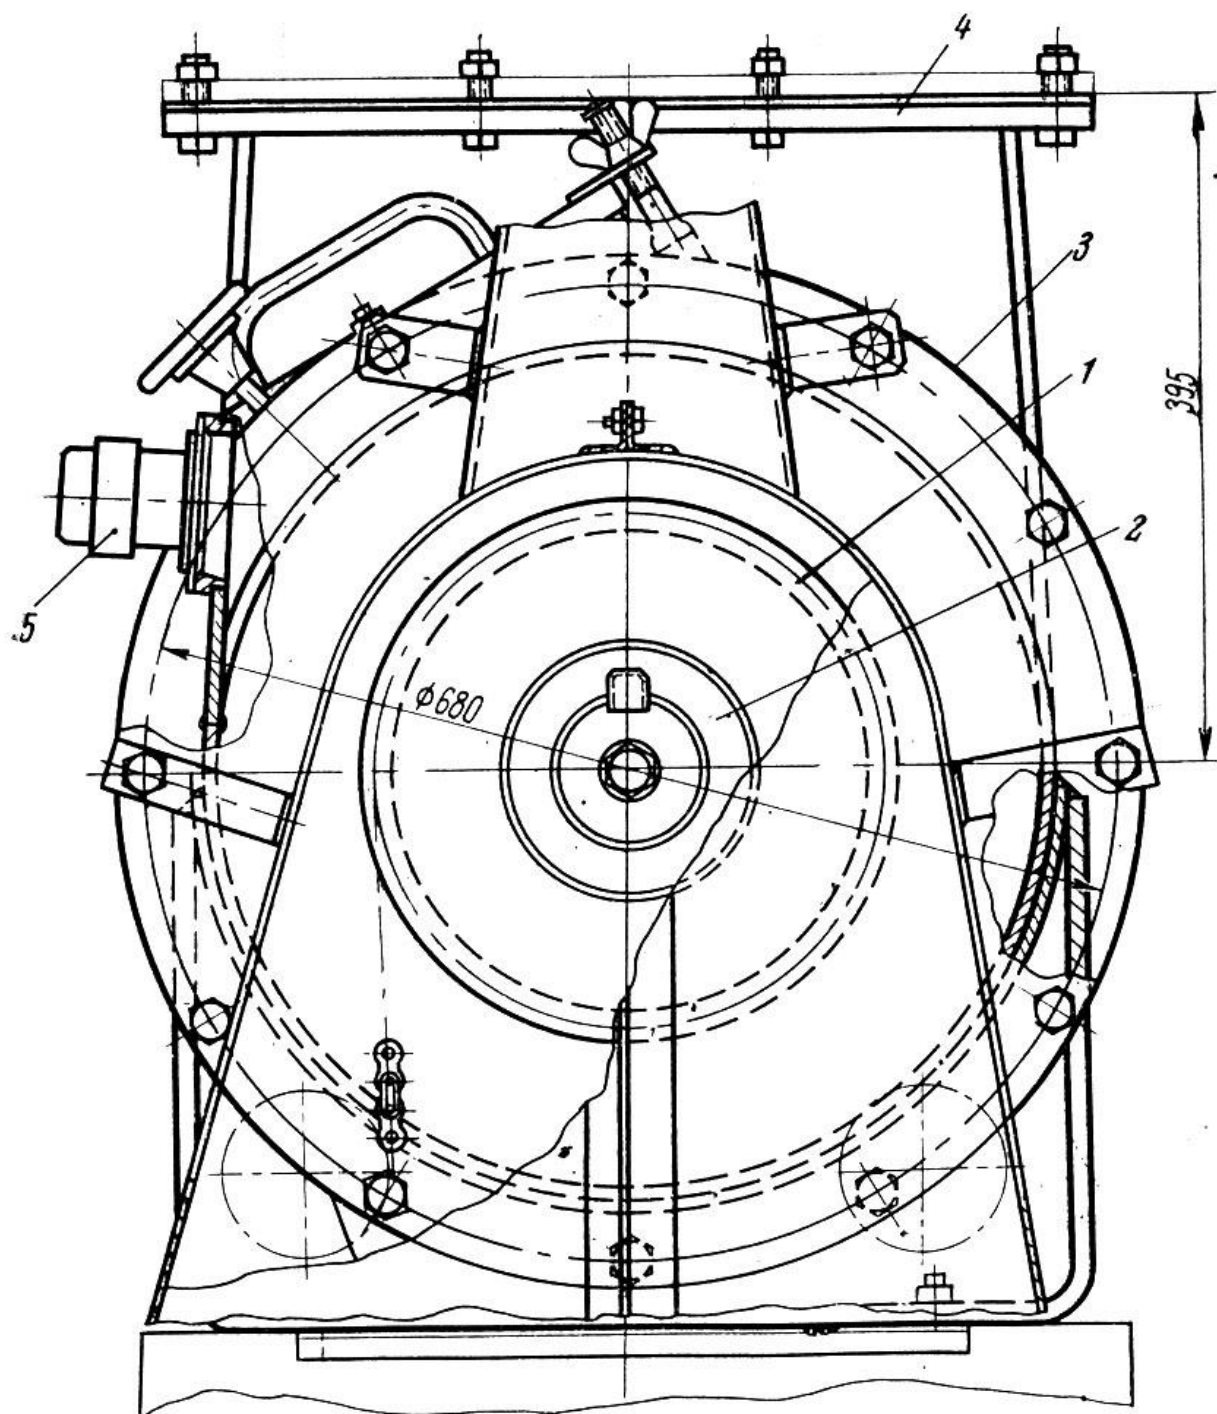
Варильник, собранный в один агрегат с прессом и сушилкой; 1 - варильник; 2 - пресс; 3 - сушилка
